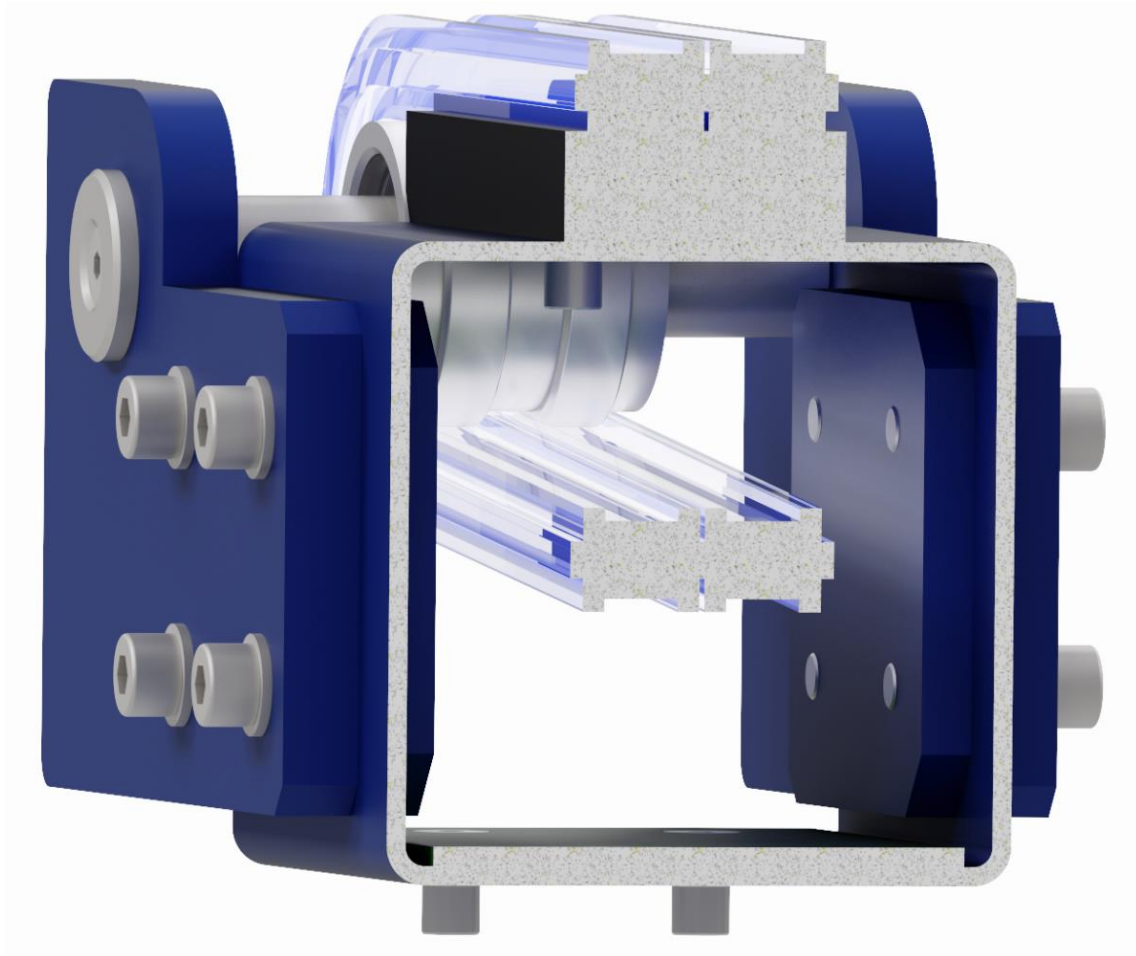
Kluzná deska uvnitř ječku [Autor]
